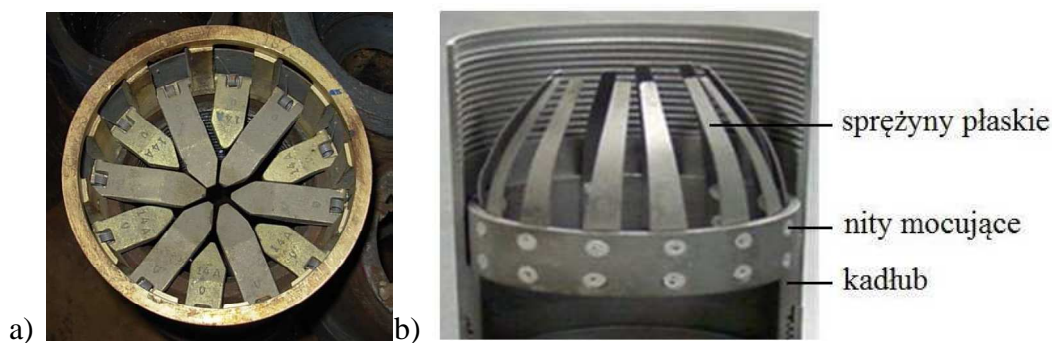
Urywki pierścieniowe. [37] [44] (fot. D. Janc)
